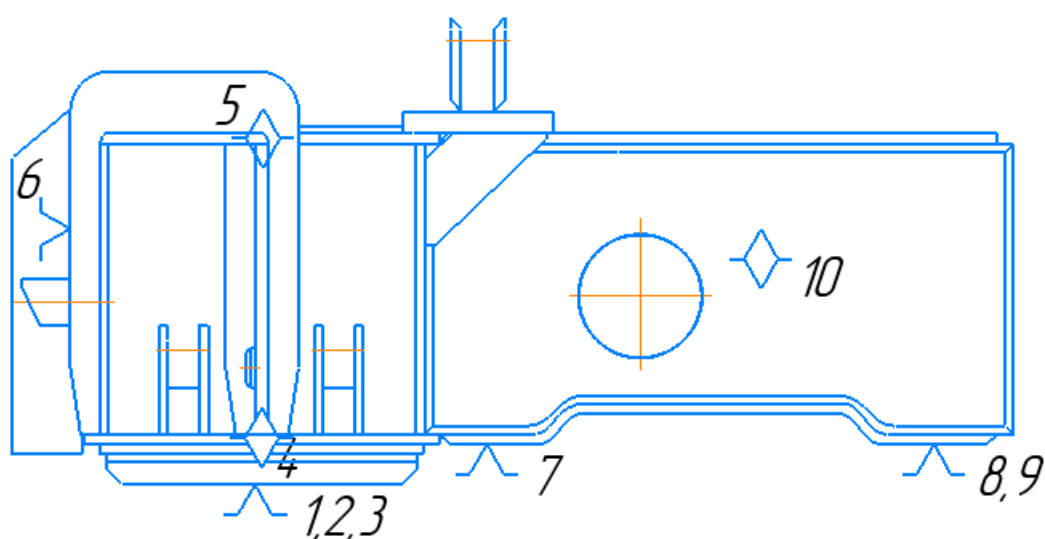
Базирование балки ФЮРА.301319.057 (вид сбоку)
